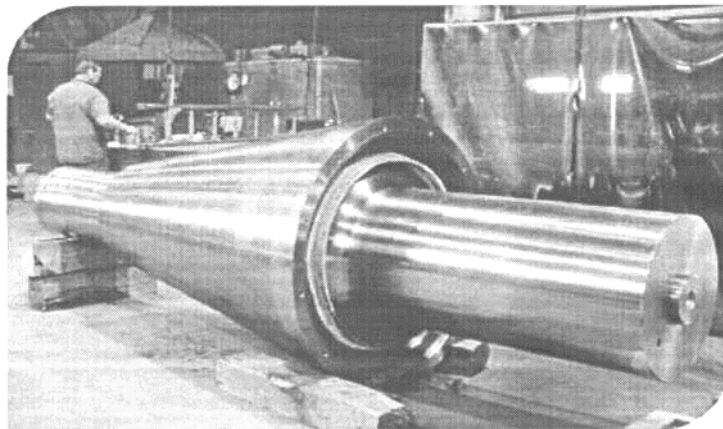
Головний вал дробарки Metso Superior МК-II 54-75
